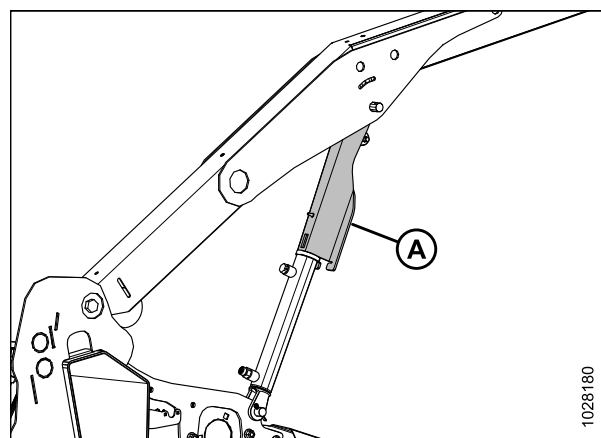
Зафиксированный предохранительный упор мотовила — наружный рычаг
